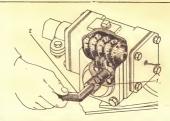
Регулировка зацепления ролика с червяком автомобиля УАЗ-691 1 — регулировочный винт; ε — илюч.
